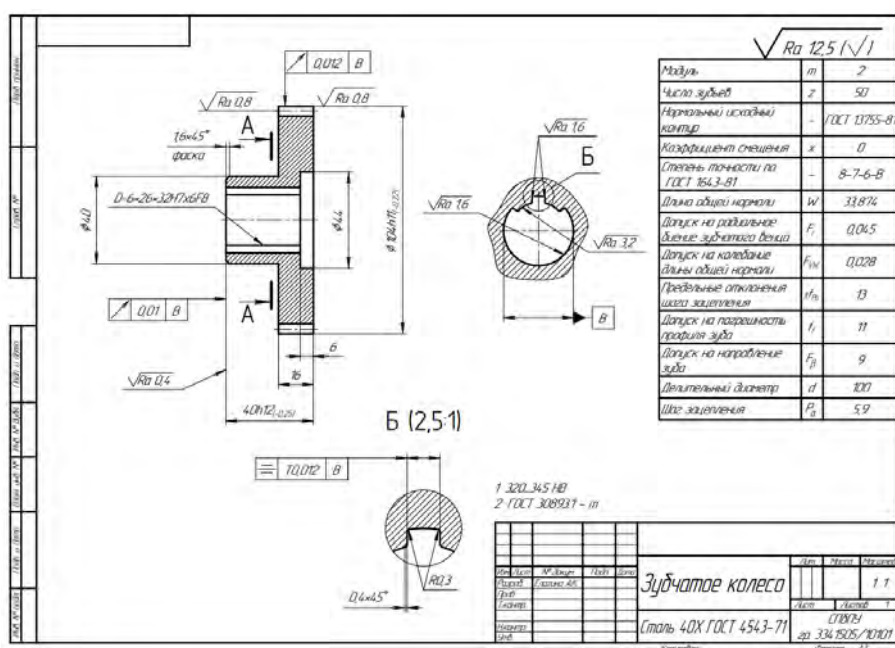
Чертеж детали «Зубчатое колесо»
